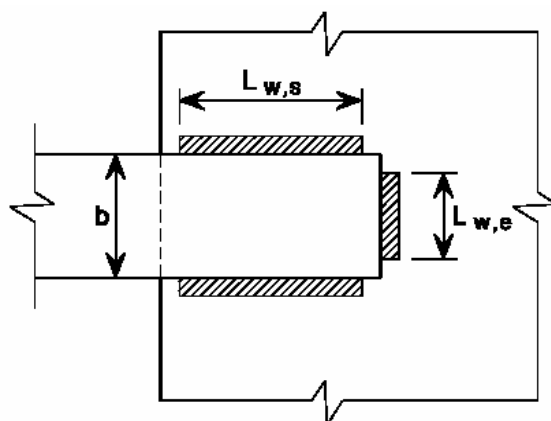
Соединение внахлест сварными угловыми швами
